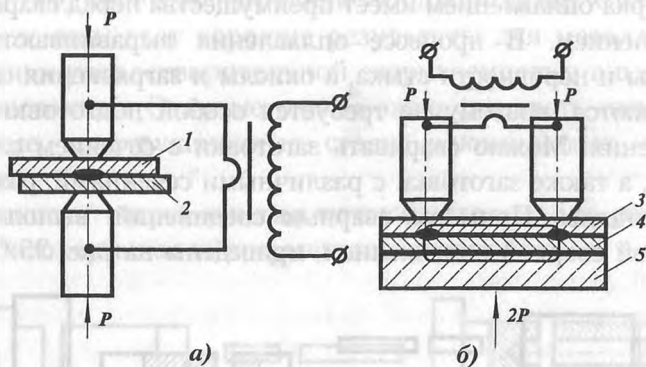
Принципиальная схема контактной сварки: а — двусторонняя; б — односторонняя
